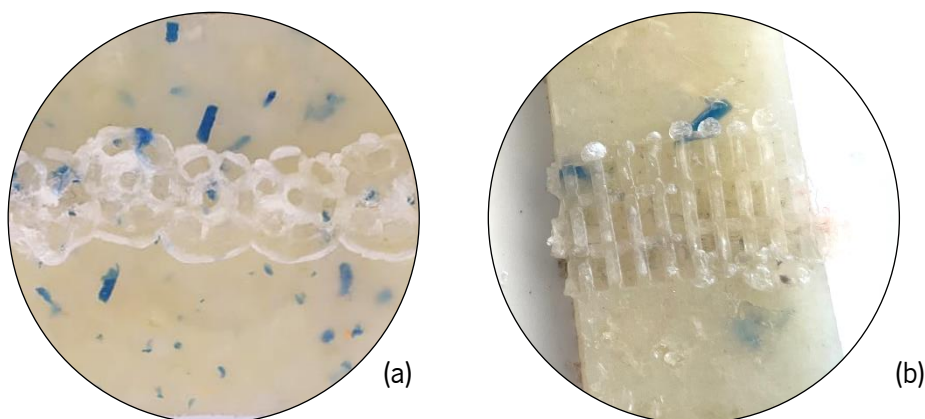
Soldadura realizada com: a) sonotrodo circular; b) sonotrodo retangular
